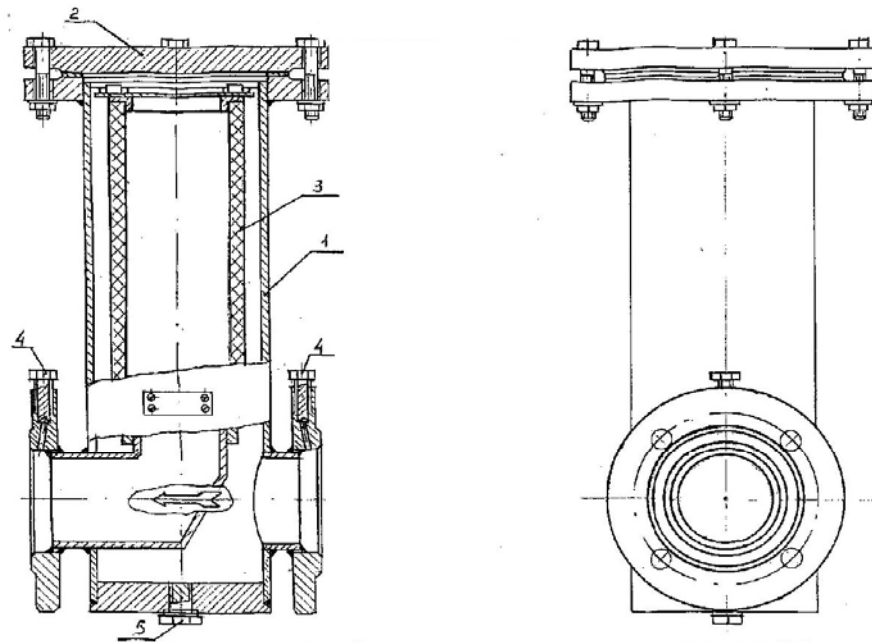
Устройство фильтра с номинальным диаметром 50, 80, 100, 125
